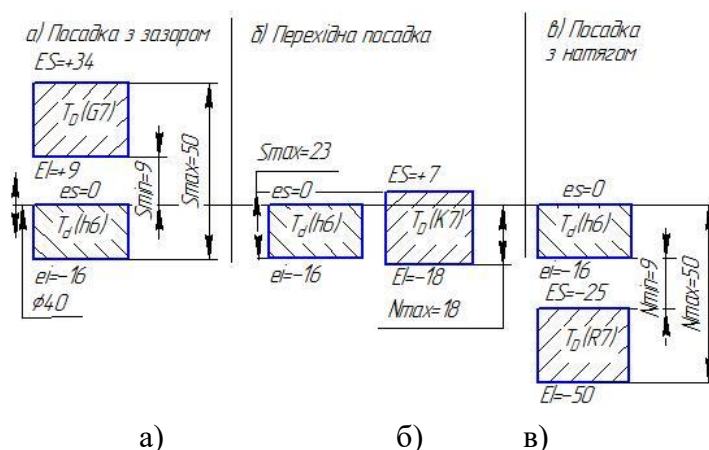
Схема розташування полів допусків посадок
